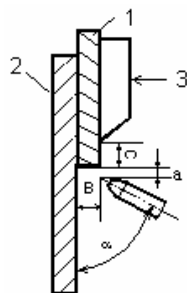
Схема процесса сварки: 1 – сталь 10Х13Г18ДУ; 2 – сталь 09Г2С; 3 – элемент, прижимающий лист нахлестки; а, в – расстояние сварочной горелки от соединяемых элементов; α - угол наклона сварочной горелки по отношению к вертикальному элементу; с – расстояние от зоны сварки до прижима
